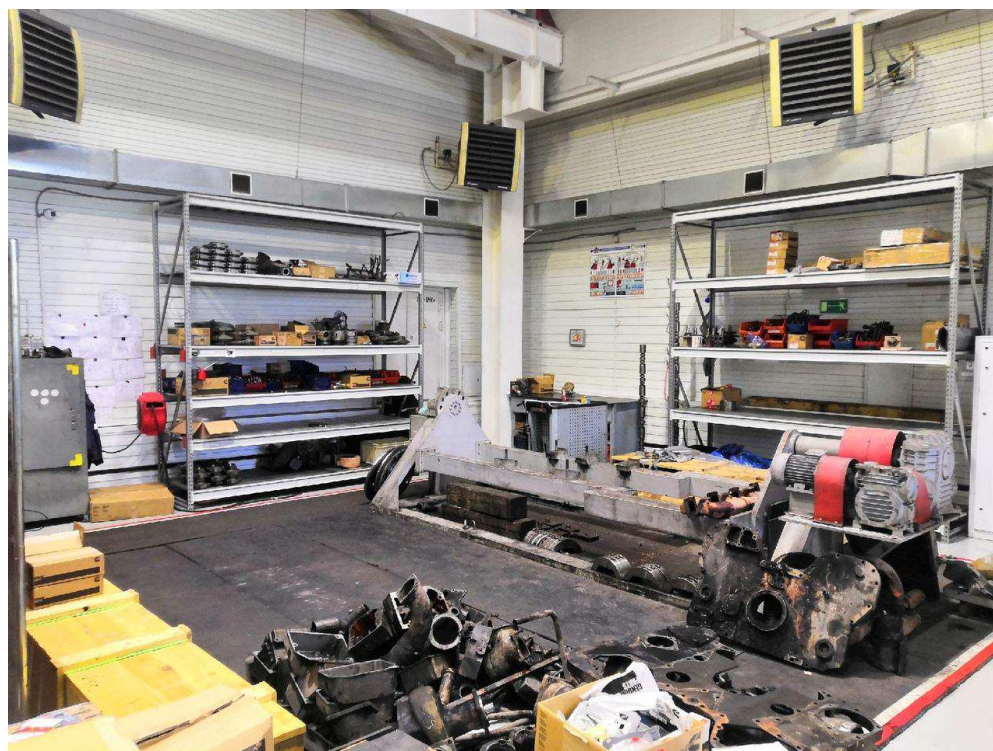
Пост разборки-сборки ДВС КТА – 50
